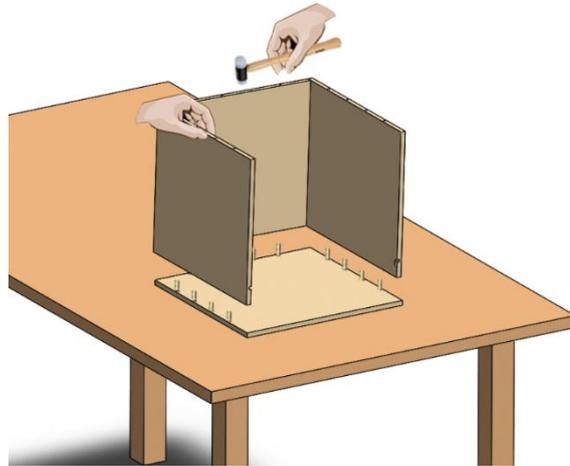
Paso 7 del ensamblaje del cajón (conjunto 2)
